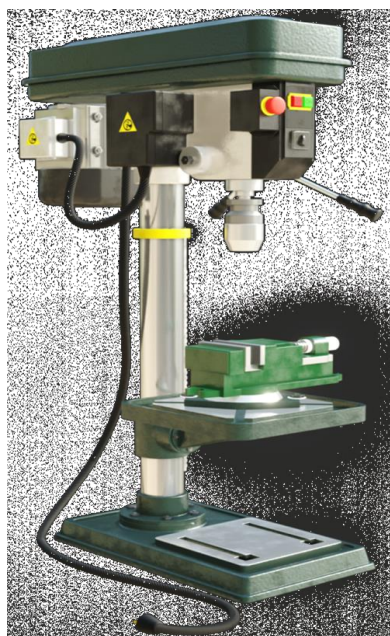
Готовая модель вертикально-сверлильного станка Quantum MC-25
